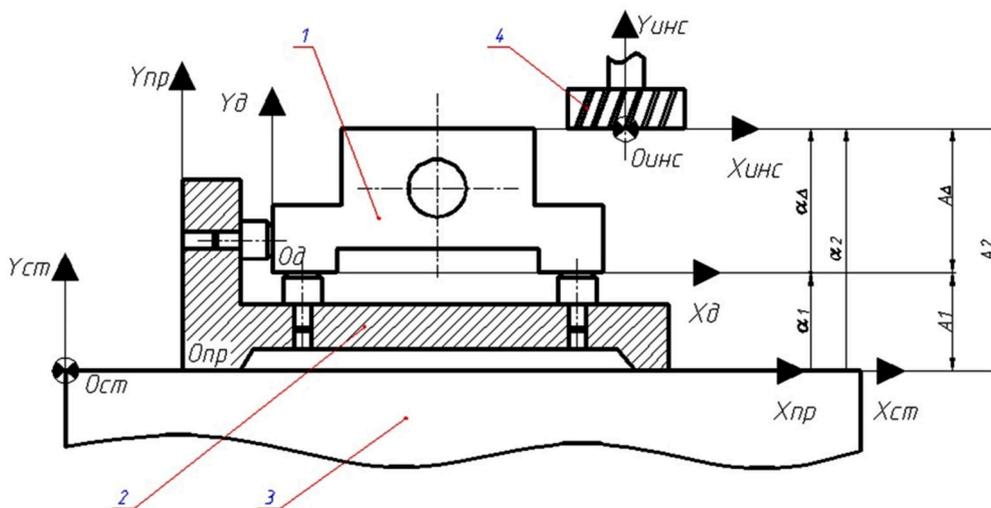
Включение обрабатываемой заготовки в размерные цепи вертикально-фрезерного станка:
